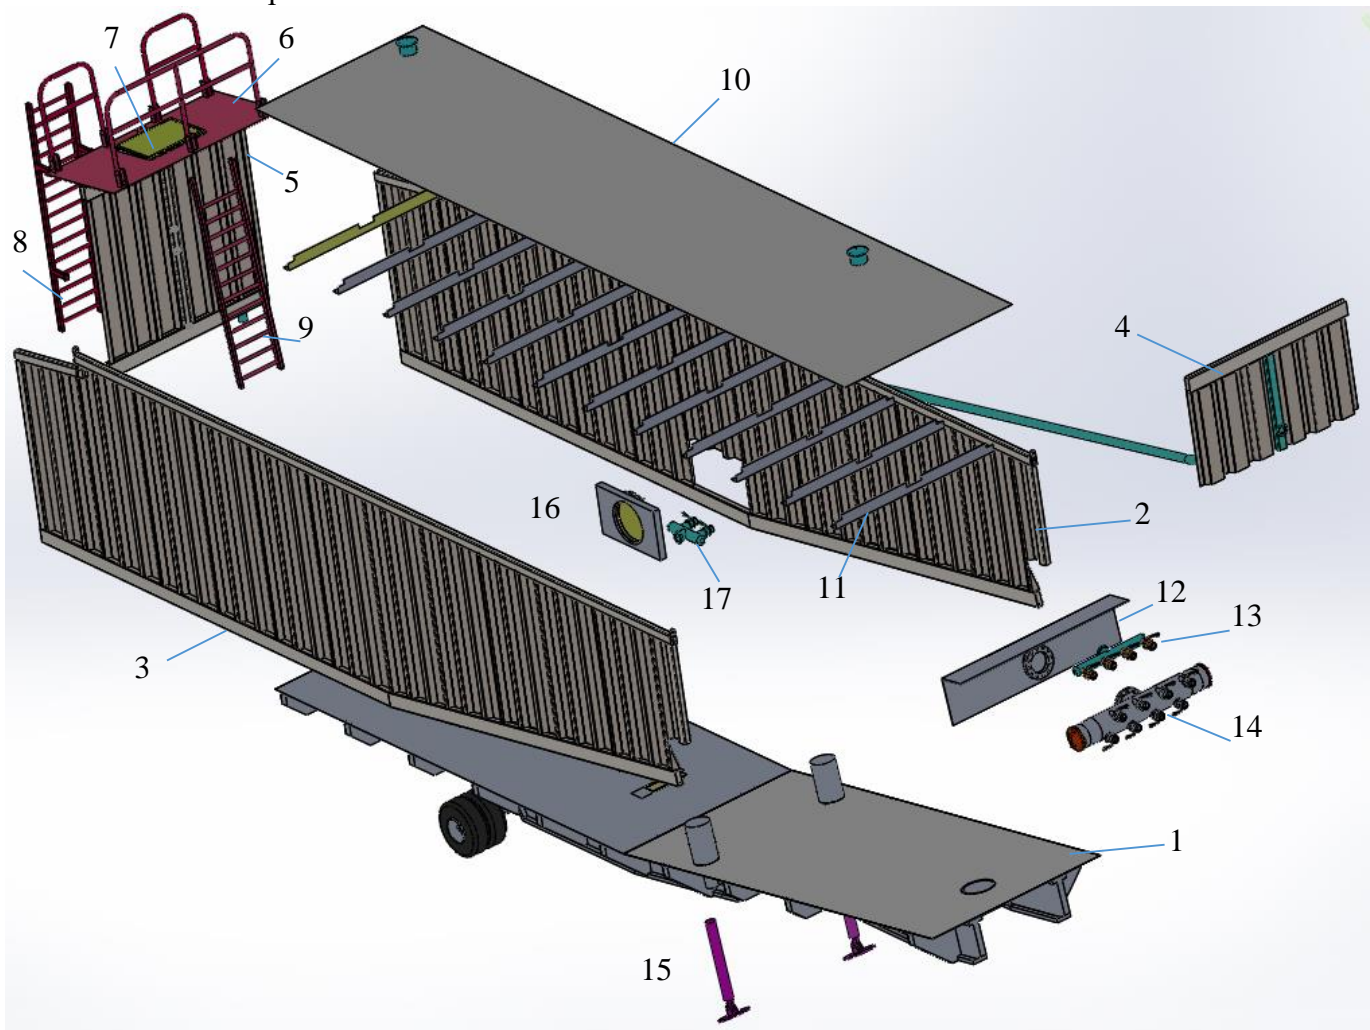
Эскизная модель полуприцепа-цистерны. Вид с разнесенными частями: 1 – шасси полуприцепа; 2 боковина левая; 3 – боковина правая; 4 – стенка передняя; 5 – стенка задняя; 6 – рабочая площадка с ограждениями; 7 – люк верхний; 8 – лестница задняя; 9 – лестница внутренняя. 10 –потолок с дыхательными клапанами; 11 – верхние балки; 12 –панель передняя; 13 – манифольд входной; 14- манифольд выходной; 15 – аутригеры; 16 – люк боковой; 17- манифольд боковой.
